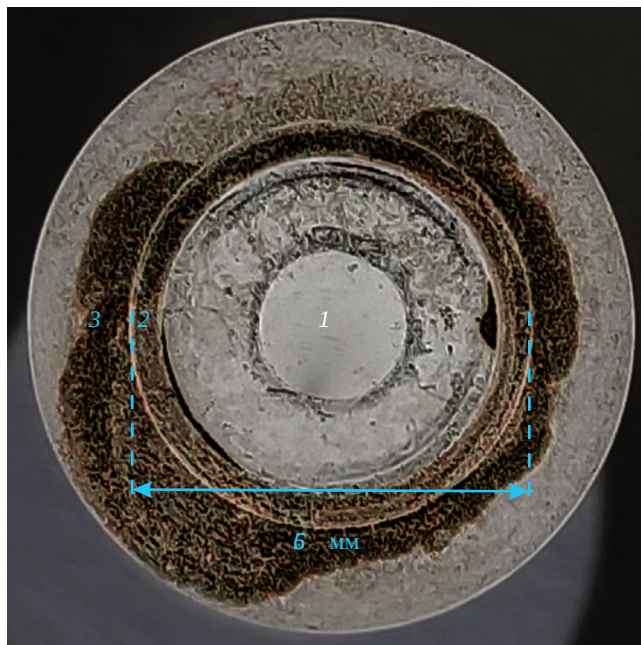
Фотография вакуумно-плотного соединения «слюдяная пластина–металл»: 1 — слюдяной диск, 2 — титановое кольцо, 3 — заготовка из псевдосплава МД-15.
